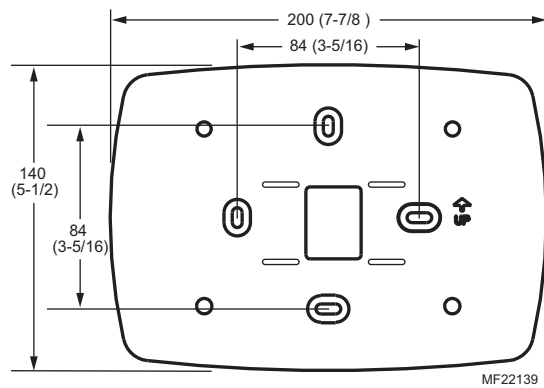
Encombrement de la plaque de recouvrement 32003796-001 en mm (po).
